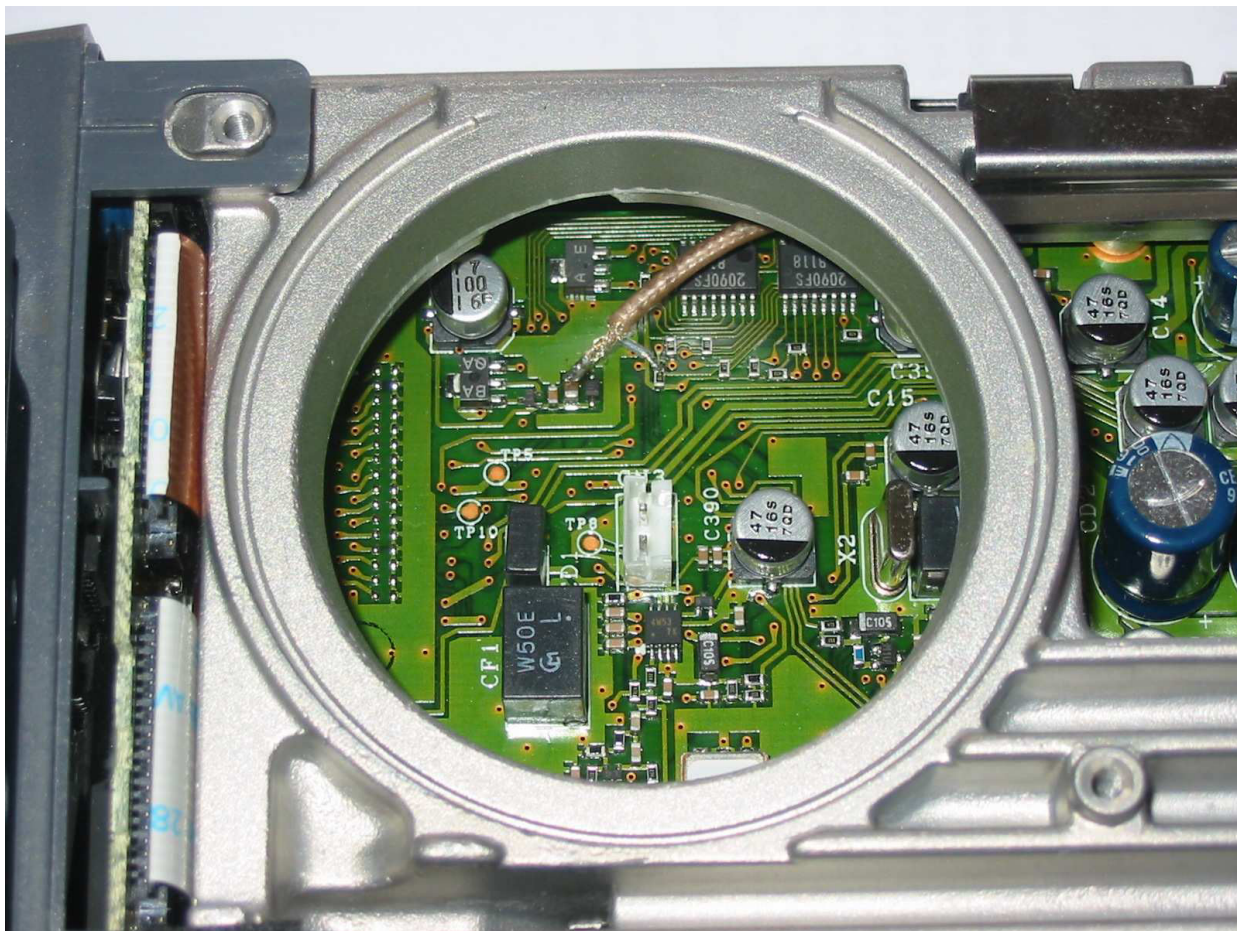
Vue de dessus du TM-V7. La face avant est à gauche. Le haut-parleur a été enlevé. On voit le câble qui a été ajouté, qui est soudé sur deux composants, puis qui part de l'autre côté de la carte. La mise en place et la soudure de ce câble peut être réalisée au travers du trou du haut parleur, sans démonter plus le TM-V7
